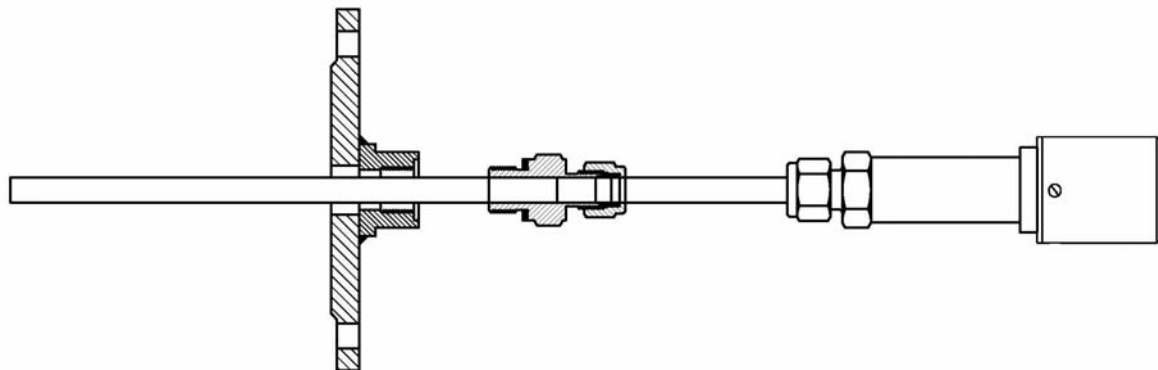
Установка штуцера установочного, медной прокладки и крышки фланца с приваренной бобышкой
